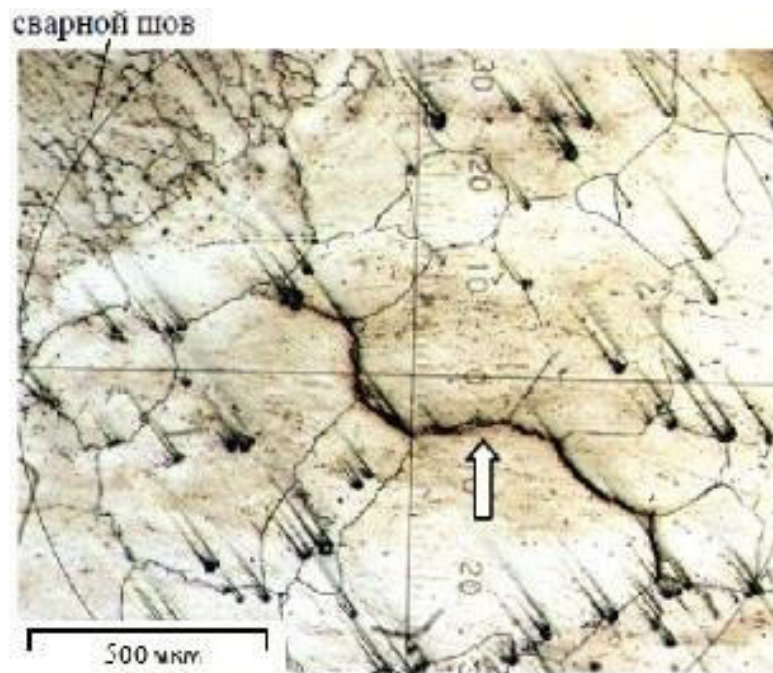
Трещина в ЗТВ сварного соединения сплава ЭП718
